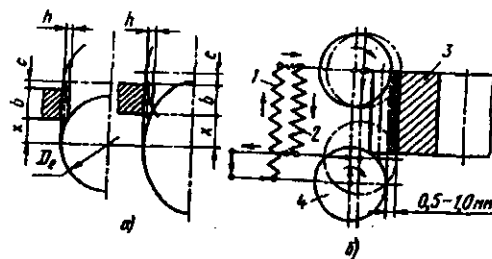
Схемы зубофрезерования: а – с осевой подачей; б – двухпроходным методом
